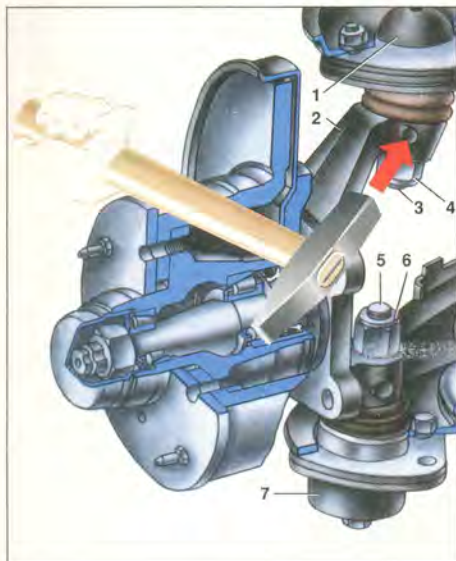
Фрагмент передней подвески "Жигулей": 1 — верхний шарнир; 2 — поворотный кулак; 3 — палец верхнего шарнира; 4, 6 — гайки; 5 — палец нижнего шарнира; 7 — нижний шарнир.
